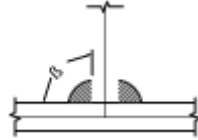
a. Unión soldada: Unión en T [6]
